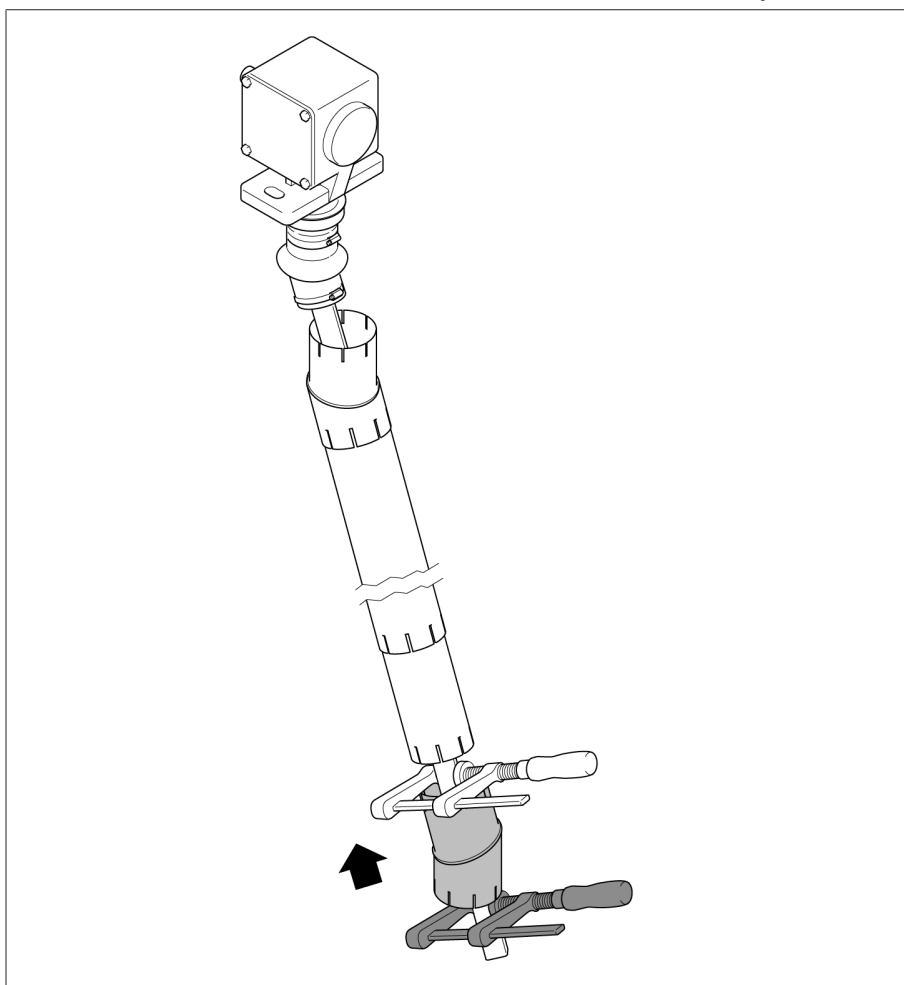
Glisser le tube de protection rotatif inférieur par-dessus le tube carré
